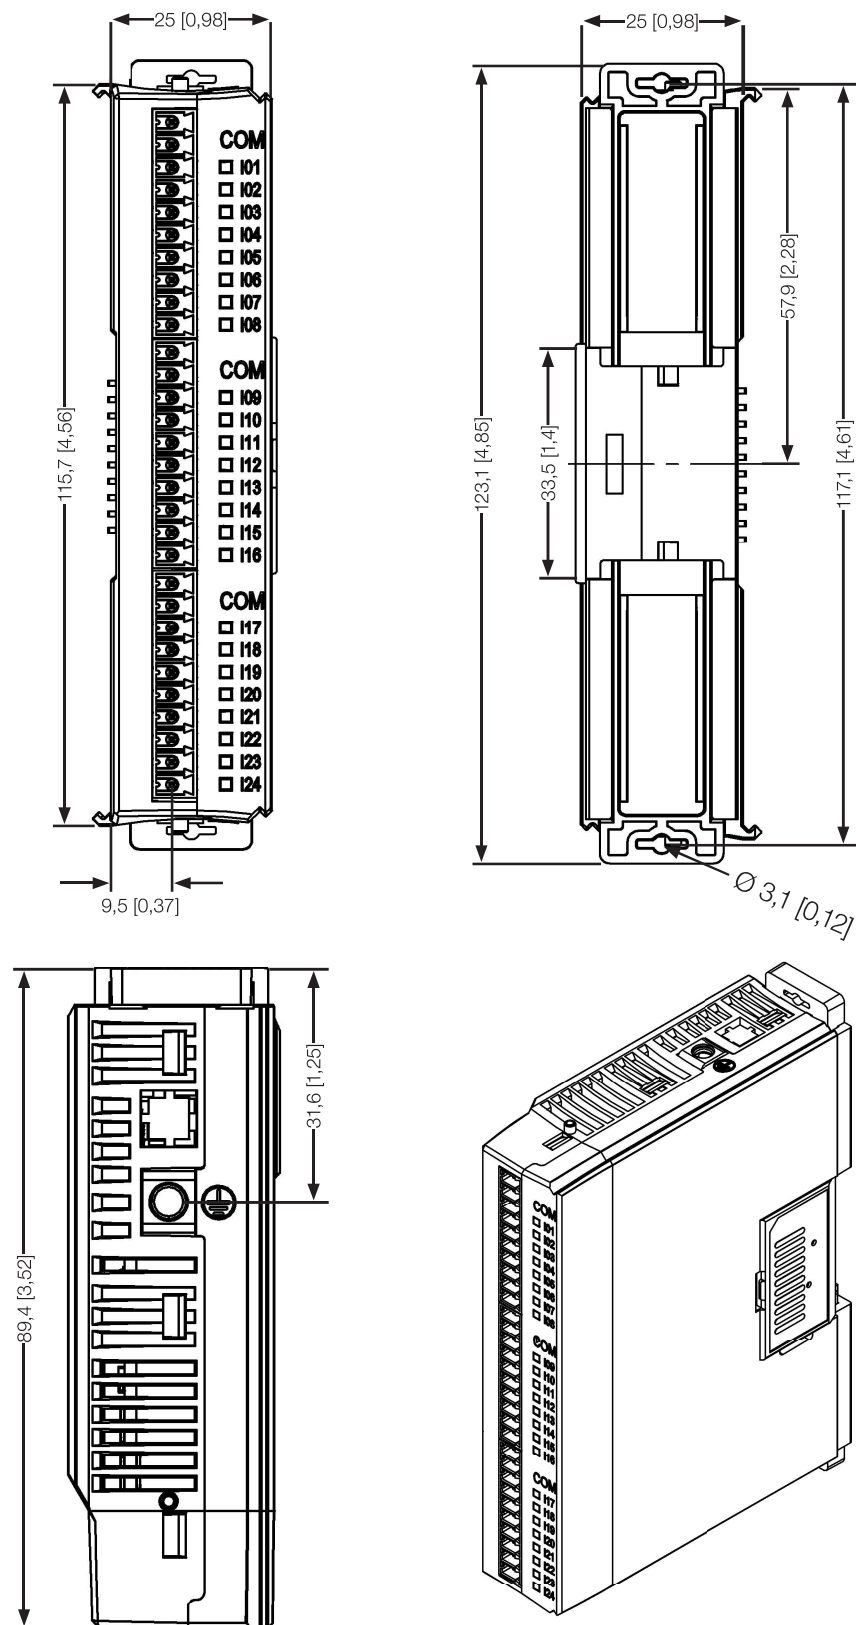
Dimensões mecânicas dos módulos de expansão em mm [in]
